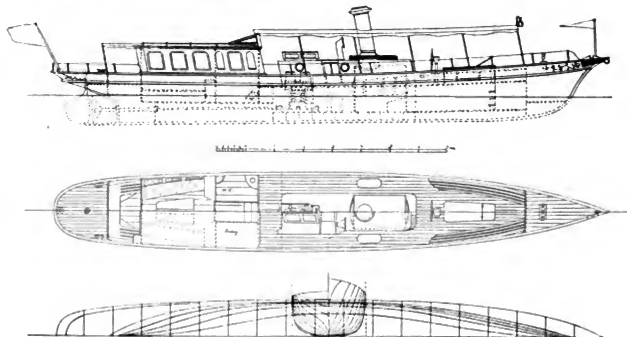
Dampfyacht für Binnengewässer von R. Holtz.
